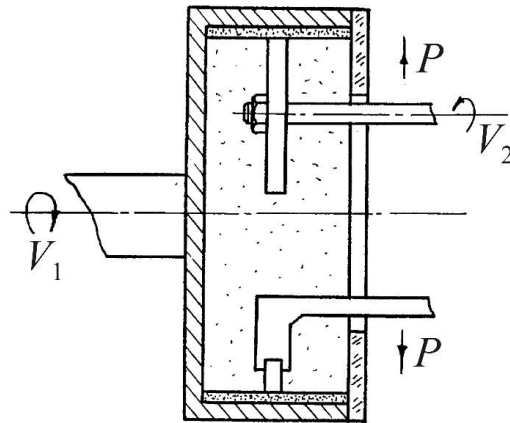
Обработка шлифовальным слоем неподвижной и вращающейся деталей
